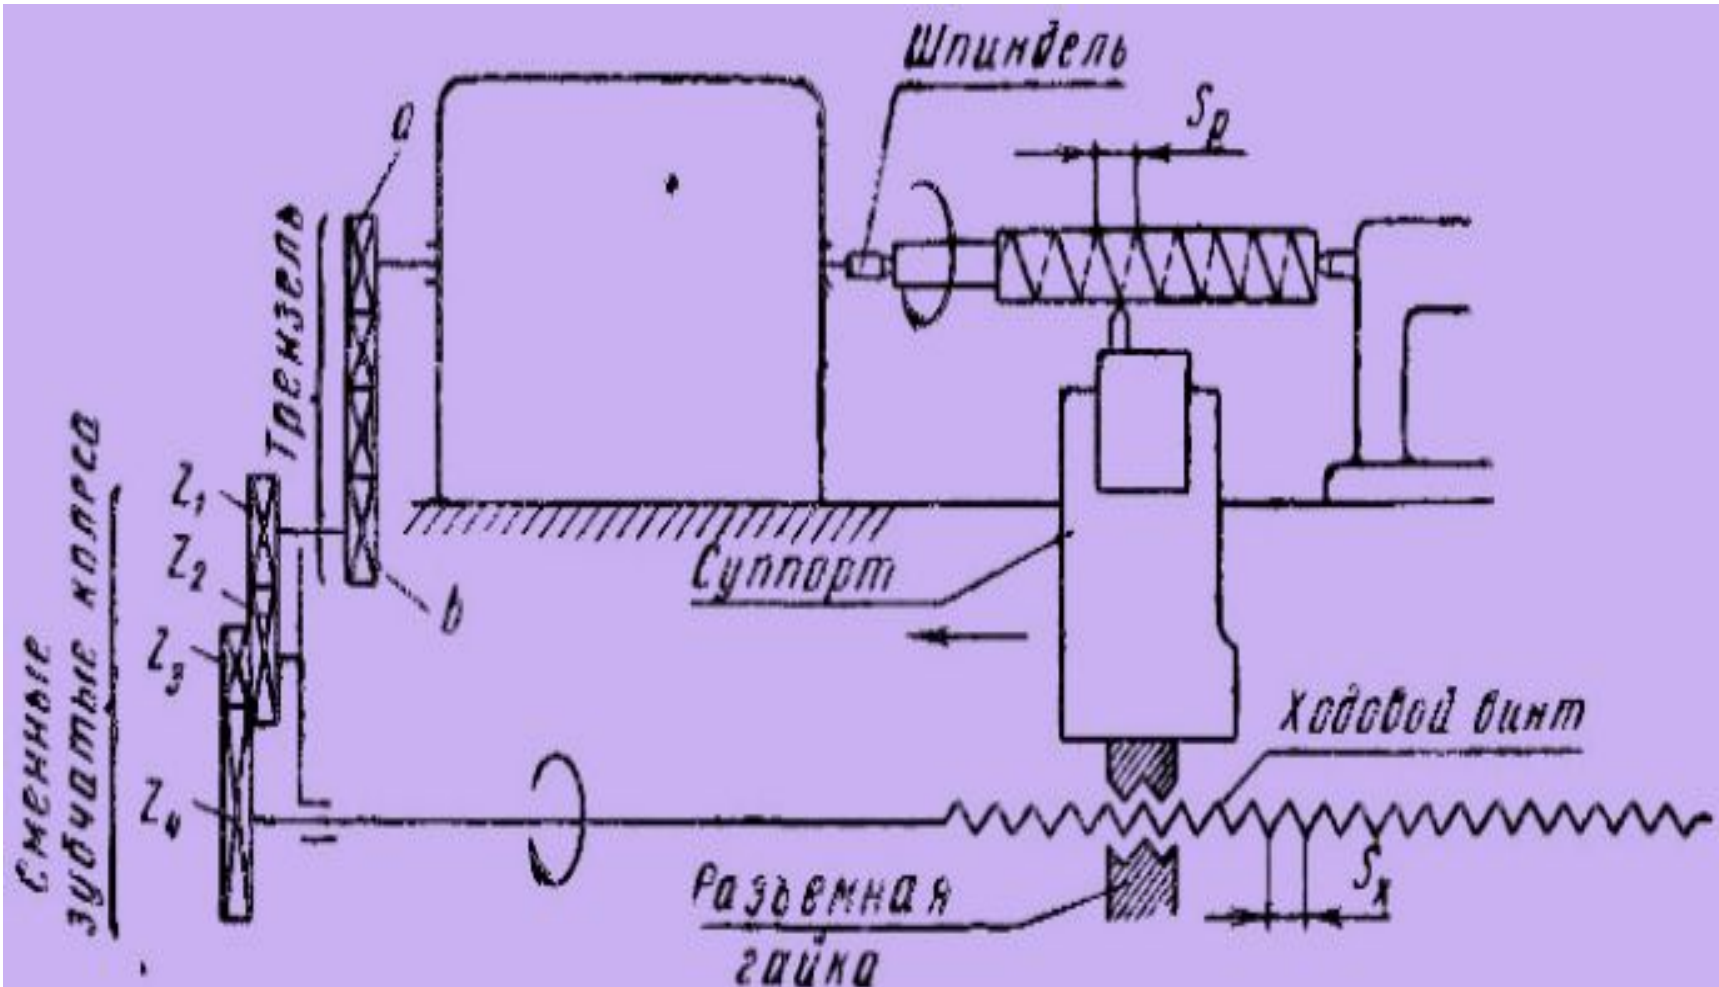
Схема передачи движения от шпинделя к ходовому винту при нарезании резьбы на токарно-винторезном станке
